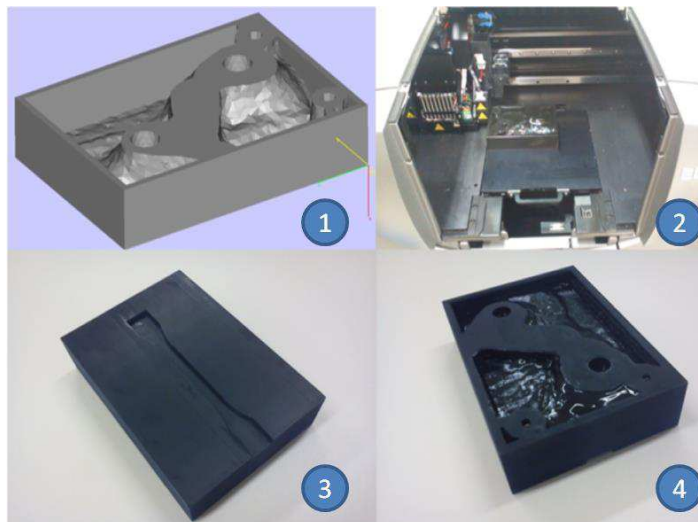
Impression sur EDEN260V de l'insert d'éprouvette
